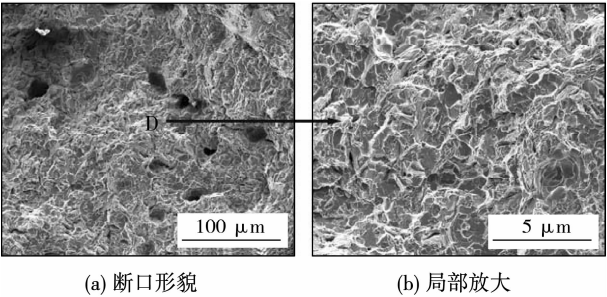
Al-Si 焊丝焊接接头断口形貌
